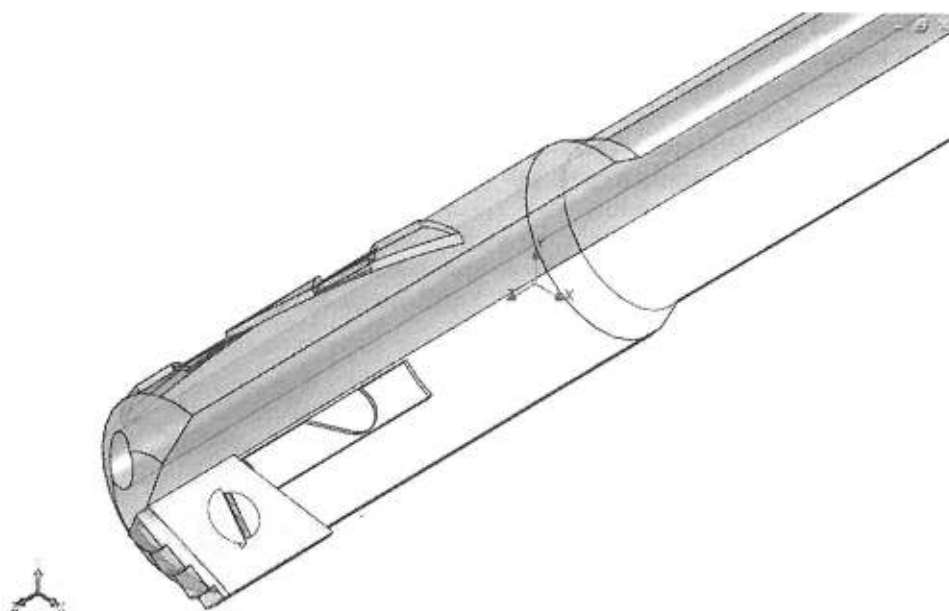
Конструкция сверла со ступенчатой режущей пластиной и дефлектором
